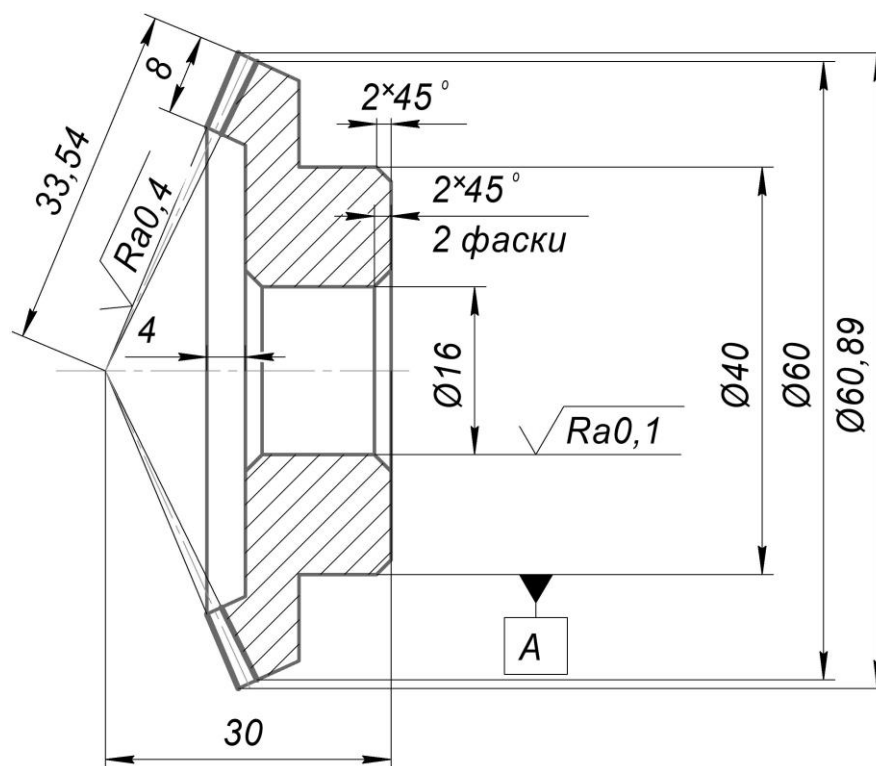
Зубчасте колесо, що оброблюється
